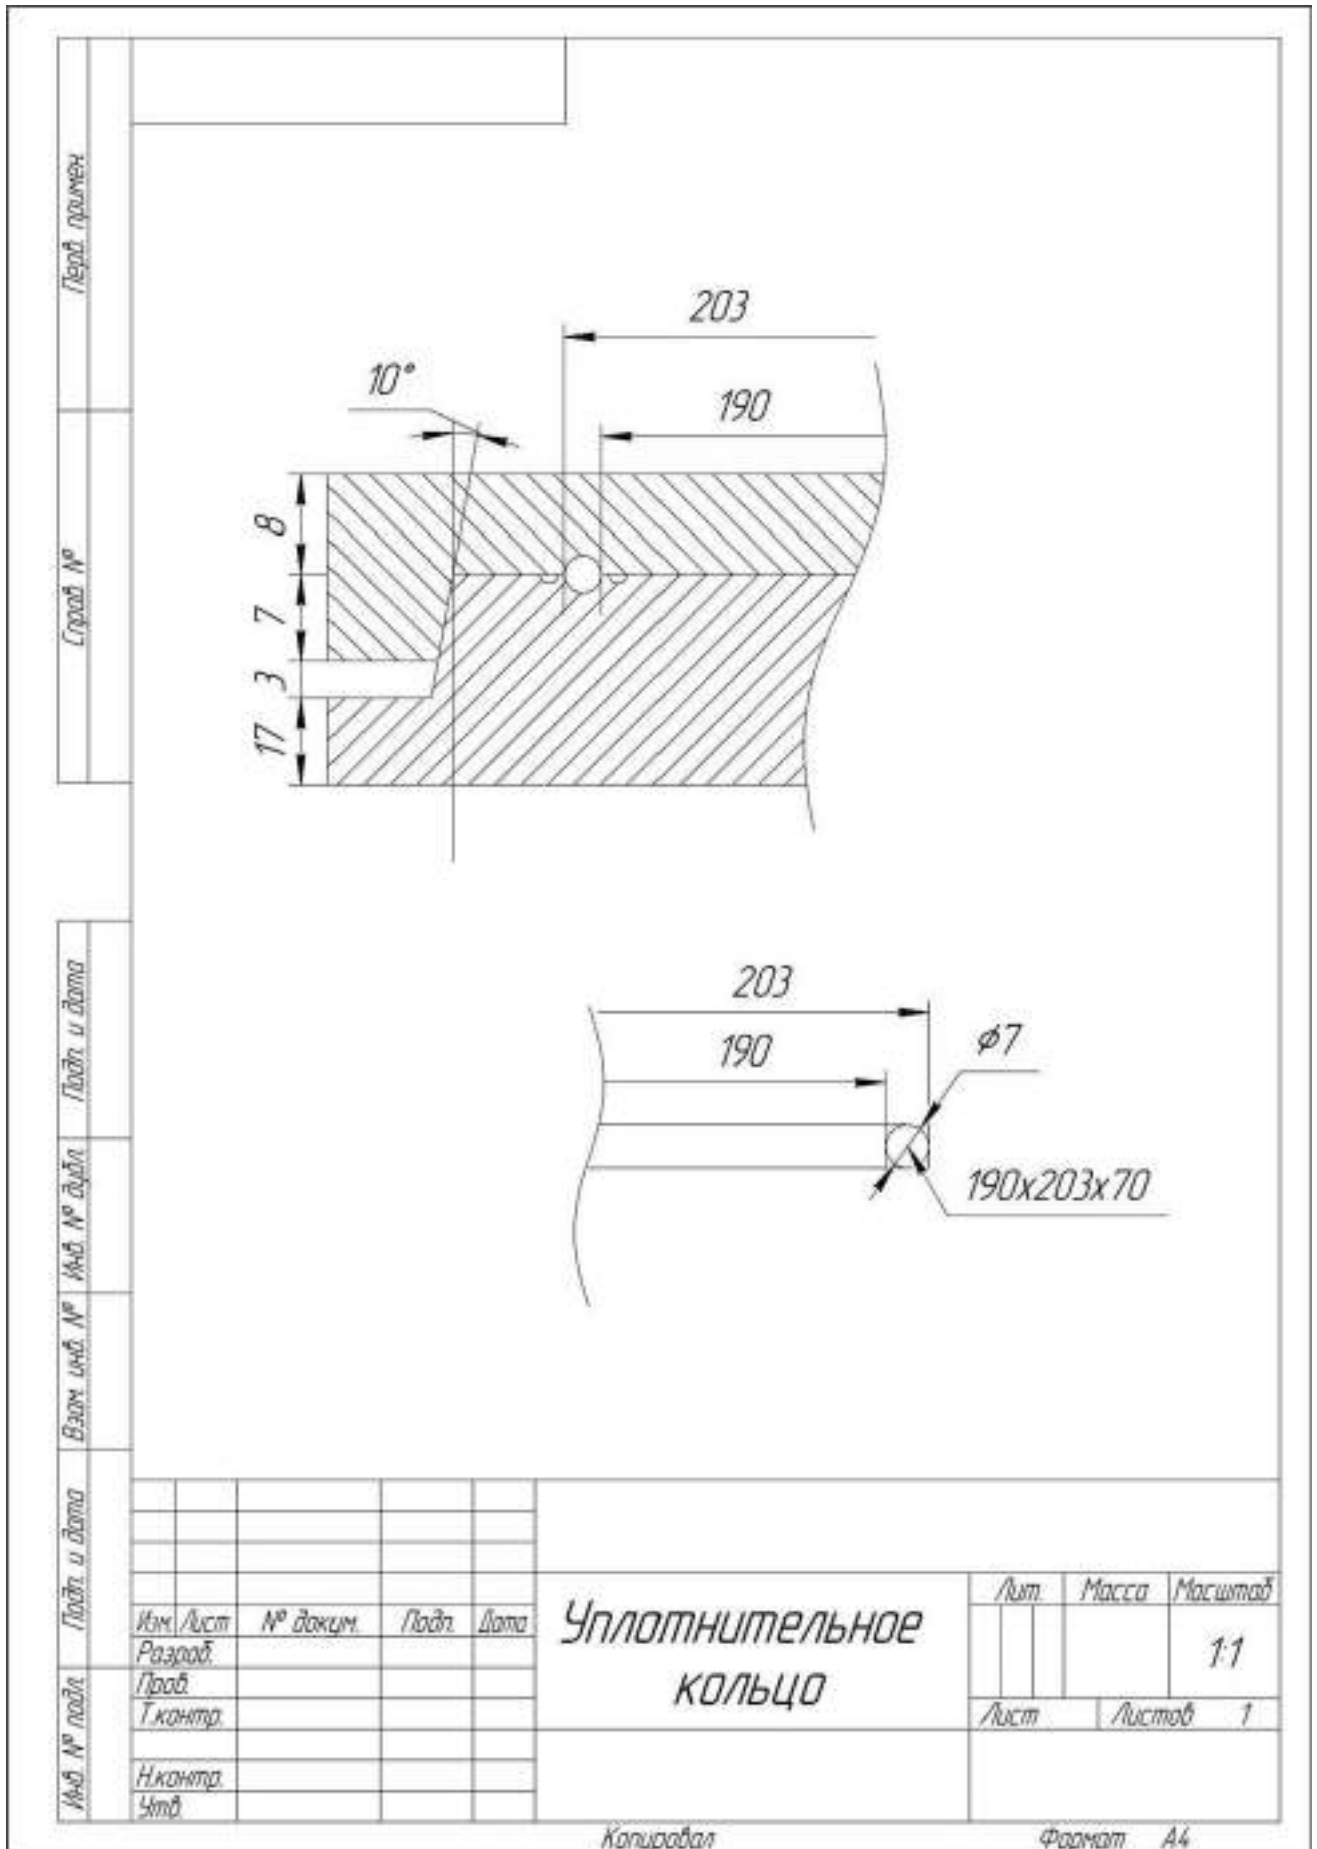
Чертеж пресс-формы для уплотнительного кольца
